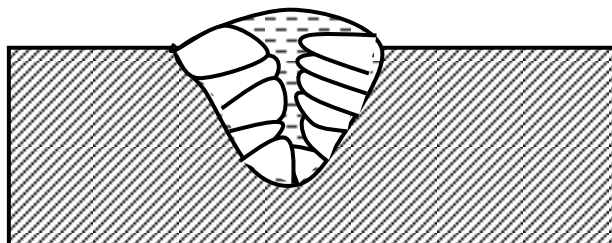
Схема роста кристаллитов в сварочной ванне
